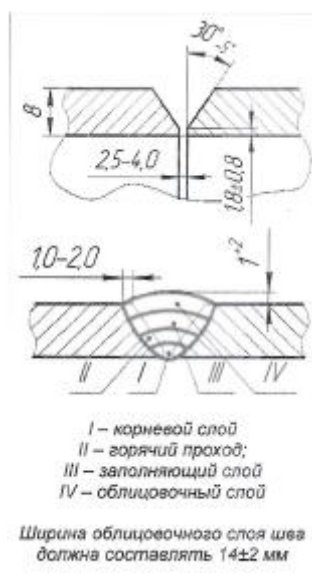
форма разделки кромок и сварного шва
